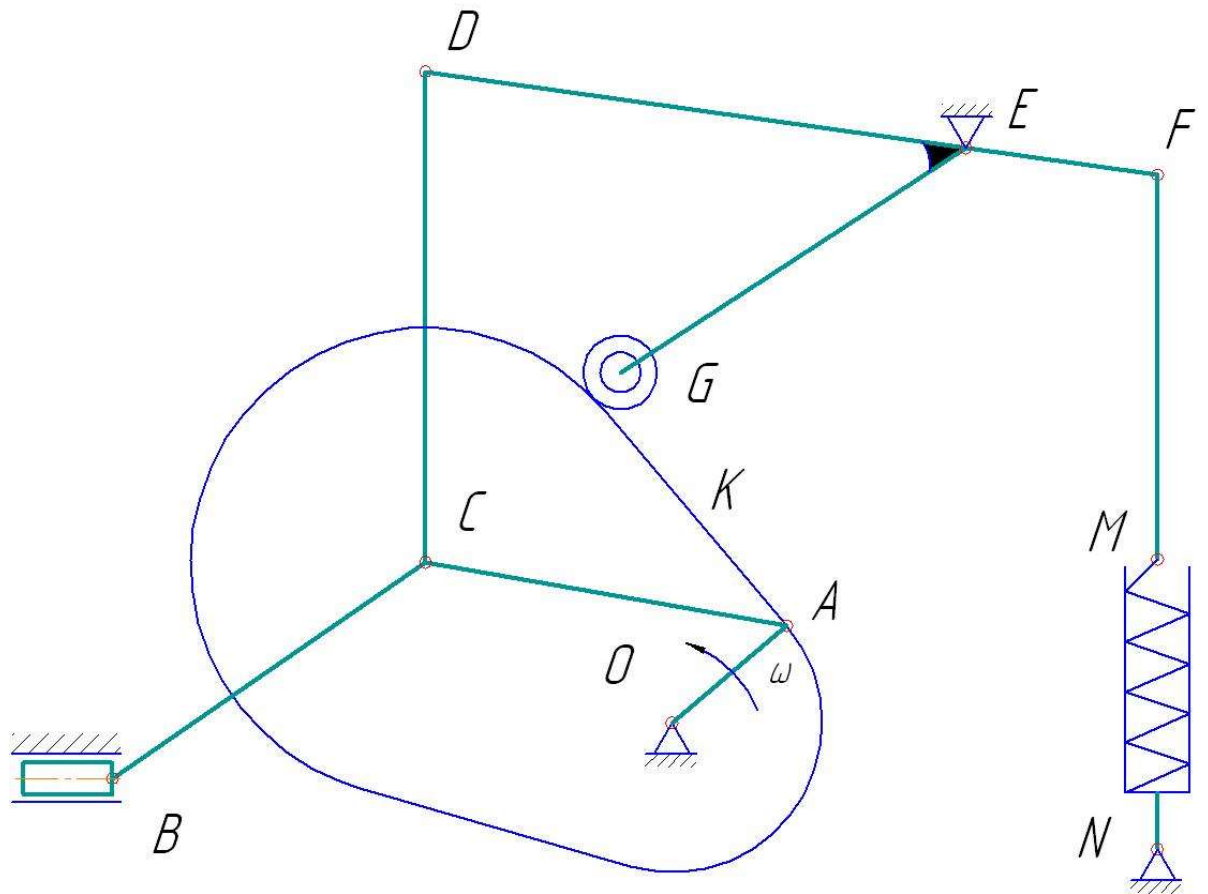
Кінематична схема механізму автомата для видавлювання
